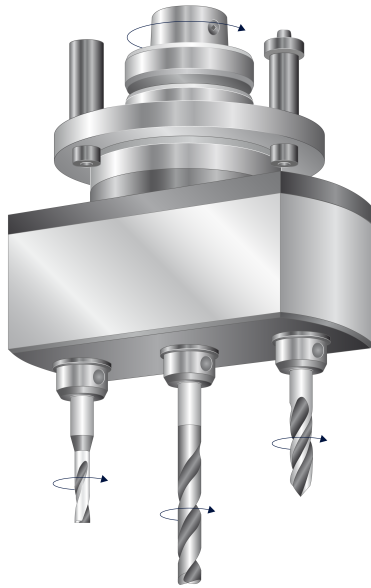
Werkzeugsystem mit mehreren Bohrern
